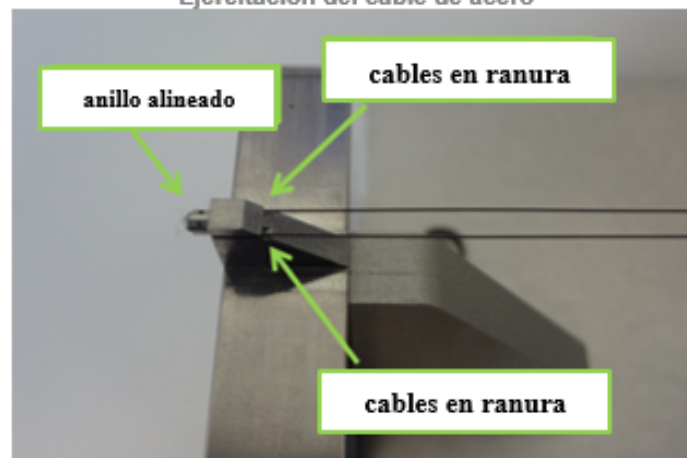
Posicionando los cables de tiraje en las abrazaderas
